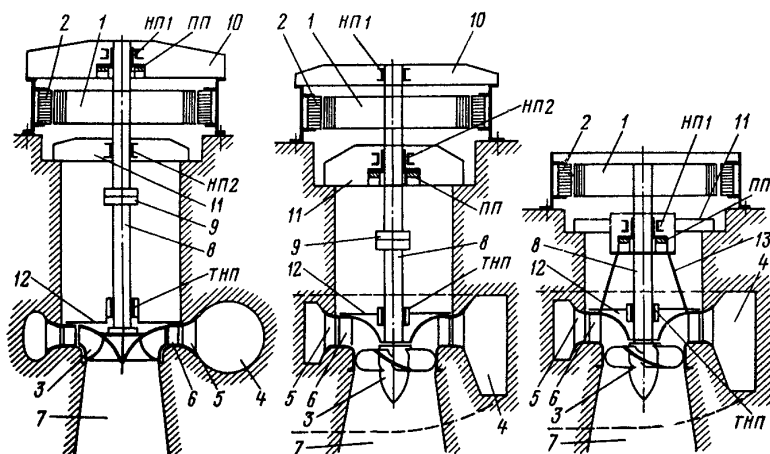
Принципиальные схемы компоновок вертикальных гидроагрегатов: 1 — ротор генератора; 2 — статор генератора; 3 — рабочее колесо; 4 — турбинная камера; 5 — статор турбины; 6 — направляющий аппарат; 7 — отсасывающая труба; 8 — вал агрегата; 9 — фланцевое соединение; 10 — верхняя крестовина; 11 — нижняя крестовина; 12 — крышка турбины; 13 — опора; НП — направляющий подшипник; ТНП — турбинный подшипник; ПП — подпятник
